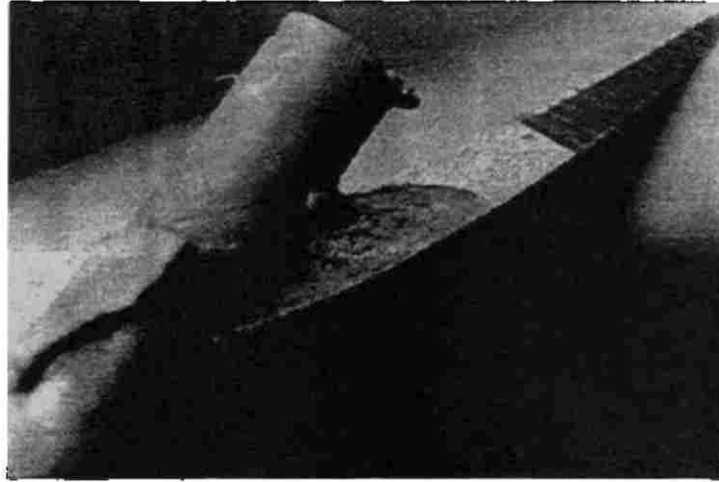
Grieta de hélice causada por daños de fatiga corrosiva.
